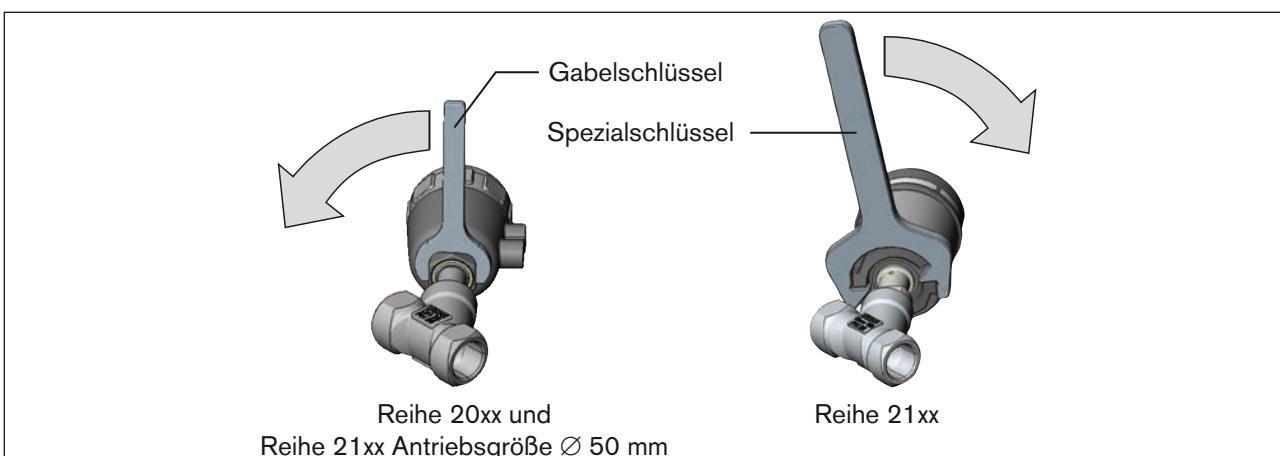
Drehen mit Spezialschlüssel / Gabelschlüssel
